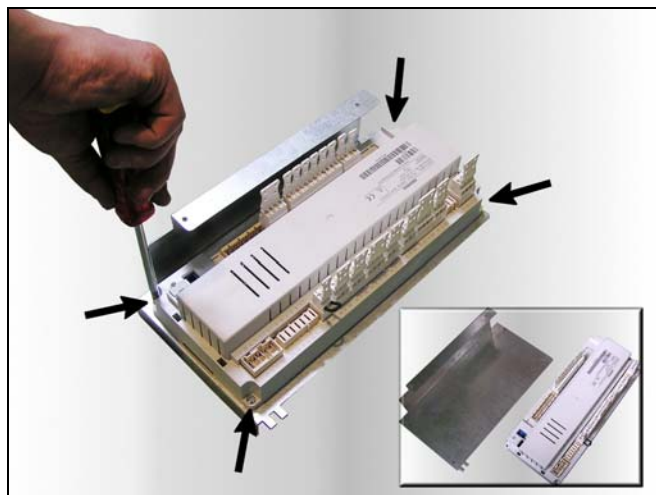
Befestigen Sie den Kesselregler mit vier Blechschrauben auf dem Regler-Halteblech.
